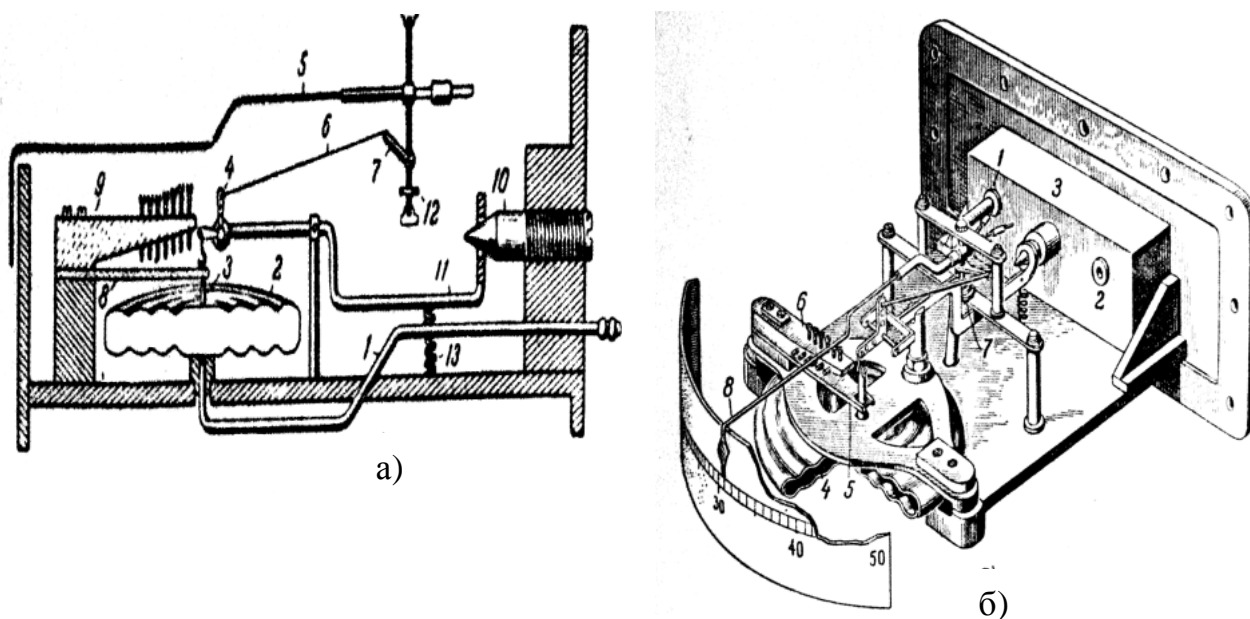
Напоромер типа НМП с горизонтальной профильной шкалой: а- схема устройства; б- внутренний вид: 1-трубка подвода давления; 2- «дыхательное» отверстие; 3- корректор нуля; 4- мембранная коробка; 5- плоская пружина; 6- кронштейн с установочными винтами; 7- спиральная пружина; 8- стрелка.
